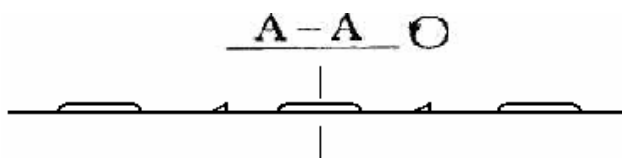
Продольный разрез внутренней боковой поверхности рабочей камеры
